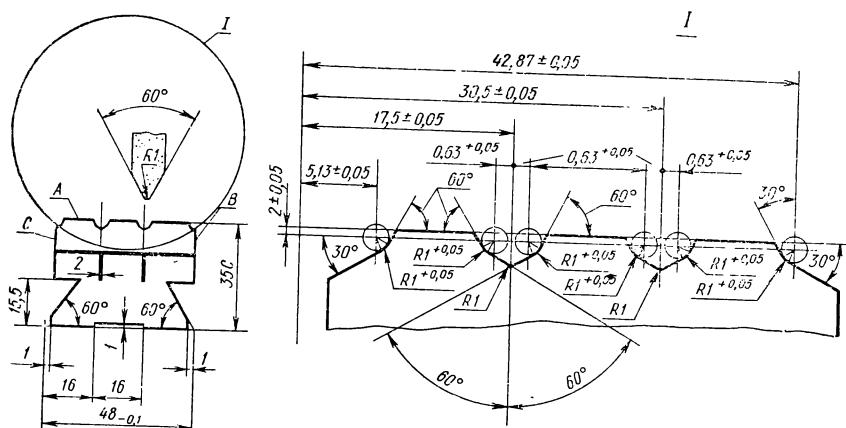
Призматический резец с симметричным расположением элементов профиля
